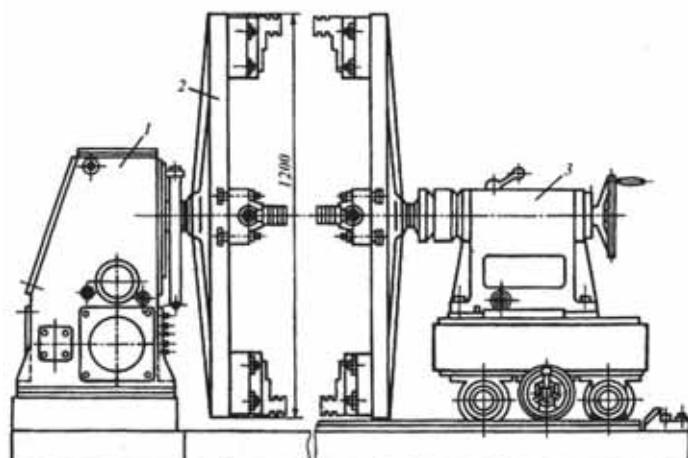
Сварочный вращатель: 1 – неподвижная стойка; 2 – планшайба; 3 – подвижная стойка
